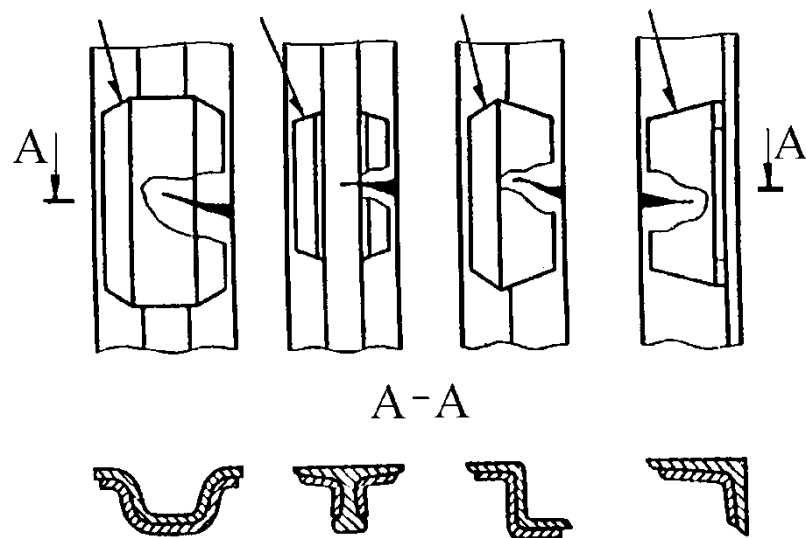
Стойки кузова вагона, усиленные профильными накладками
